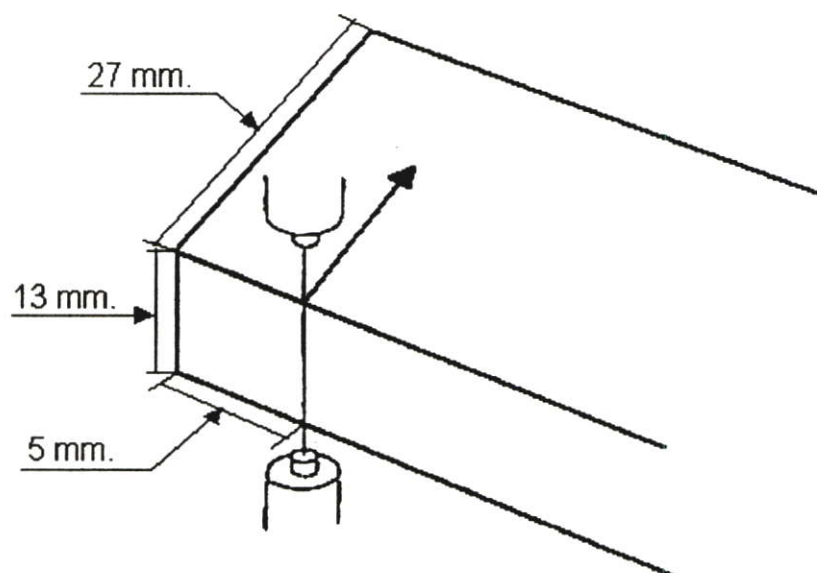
เครื่อง CNC Wire Cut EDM
